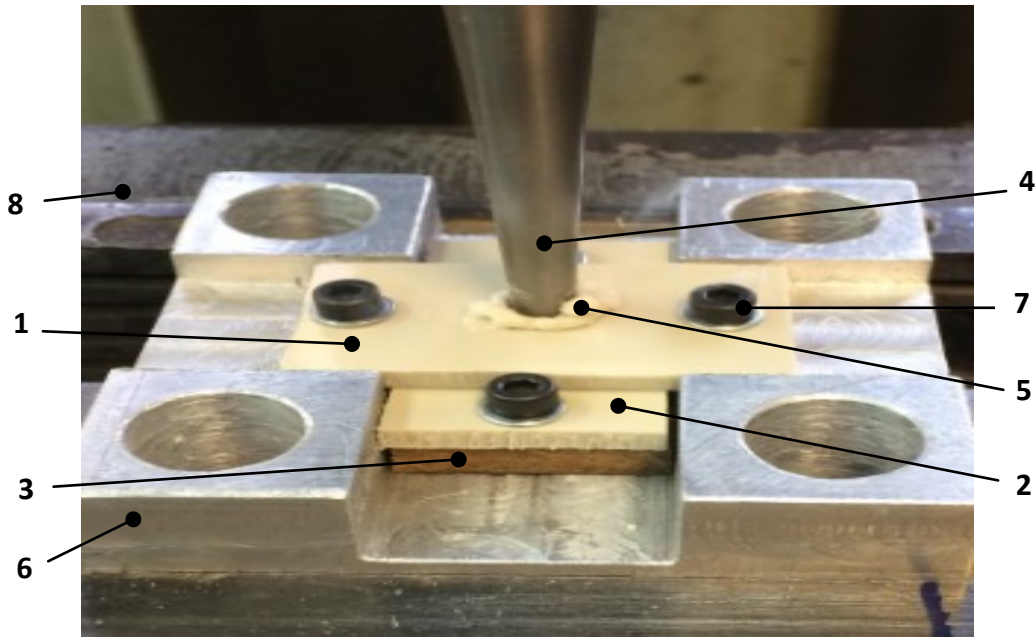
Создание образца сварного соединения полипропилена на фрезерном станке:
